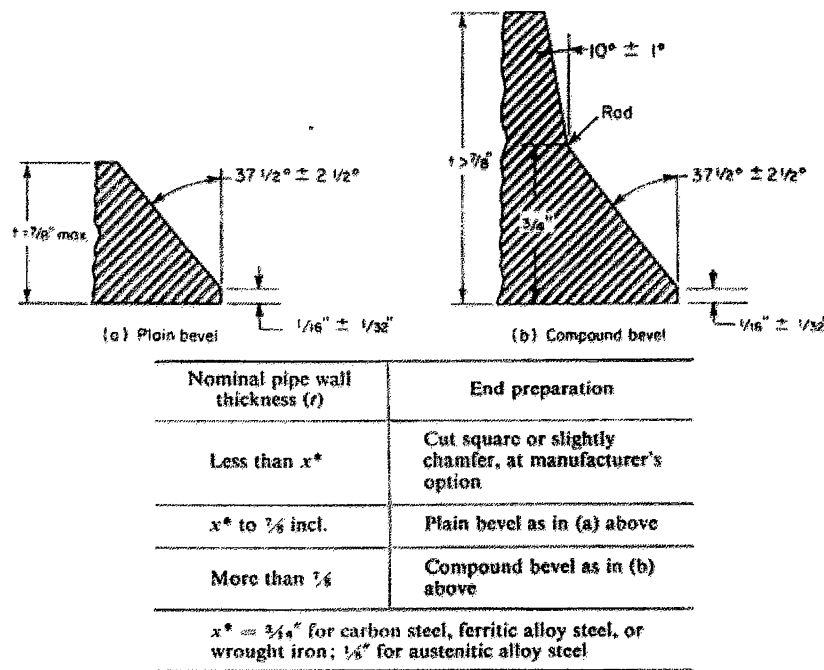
Biselado básico para todo componente a ser soldado.
